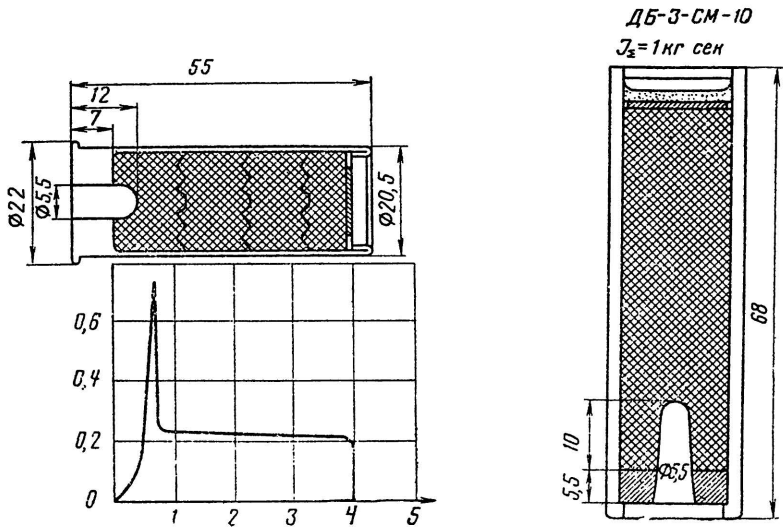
Модельный ракетный двигатель ДБ-3-СМ-10.
